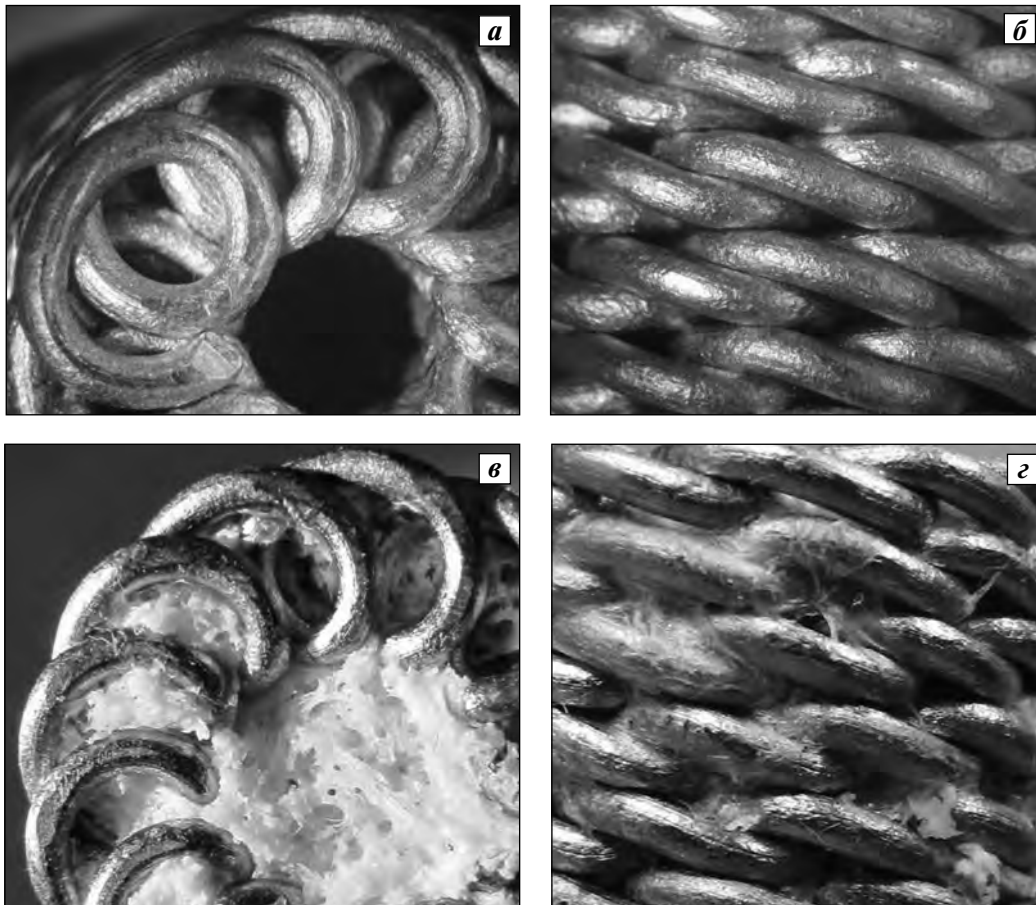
Поверхность образца, изготовленного методом диффузионной сварки титановой проволоки
